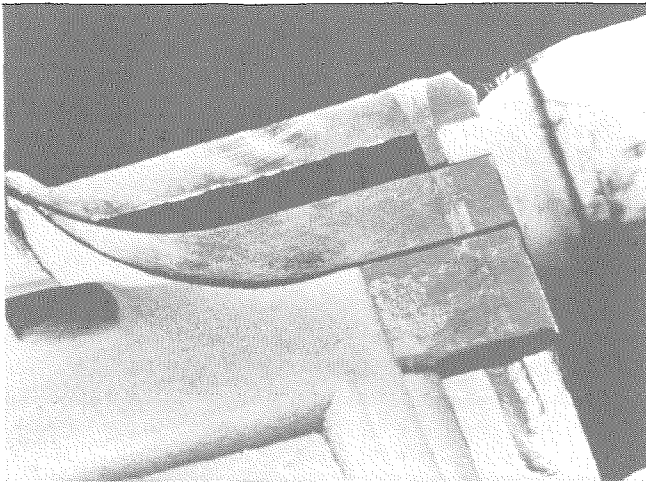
Sección típica de soldadura de diafragma del diplexor de recepción.
